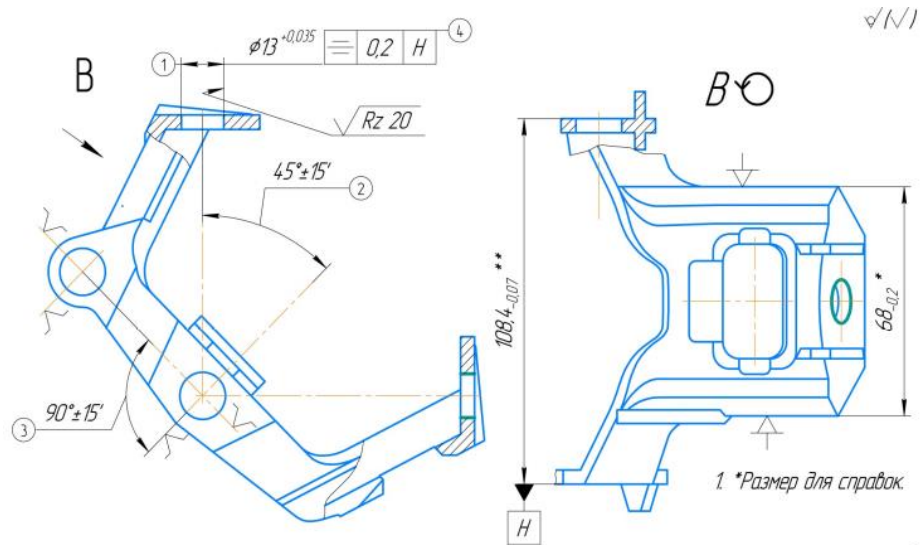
Эскиз к операции 100 – Фрезерная с ЧПУ
